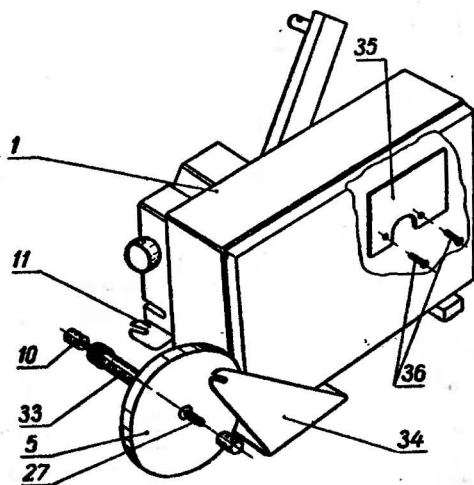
Размещение основных деталей на кинопроекторе: 1 — корпус проектора; 5 — маховик; 10 — гайка, 2 шт.; 11 — кронштейн малый; 27 — ось маховика; 33 — вал полый; 34 — кронштейн большой; 35 — плата предварительного усилителя; 36 — винты крепления колодки переключателя напряжения сети
